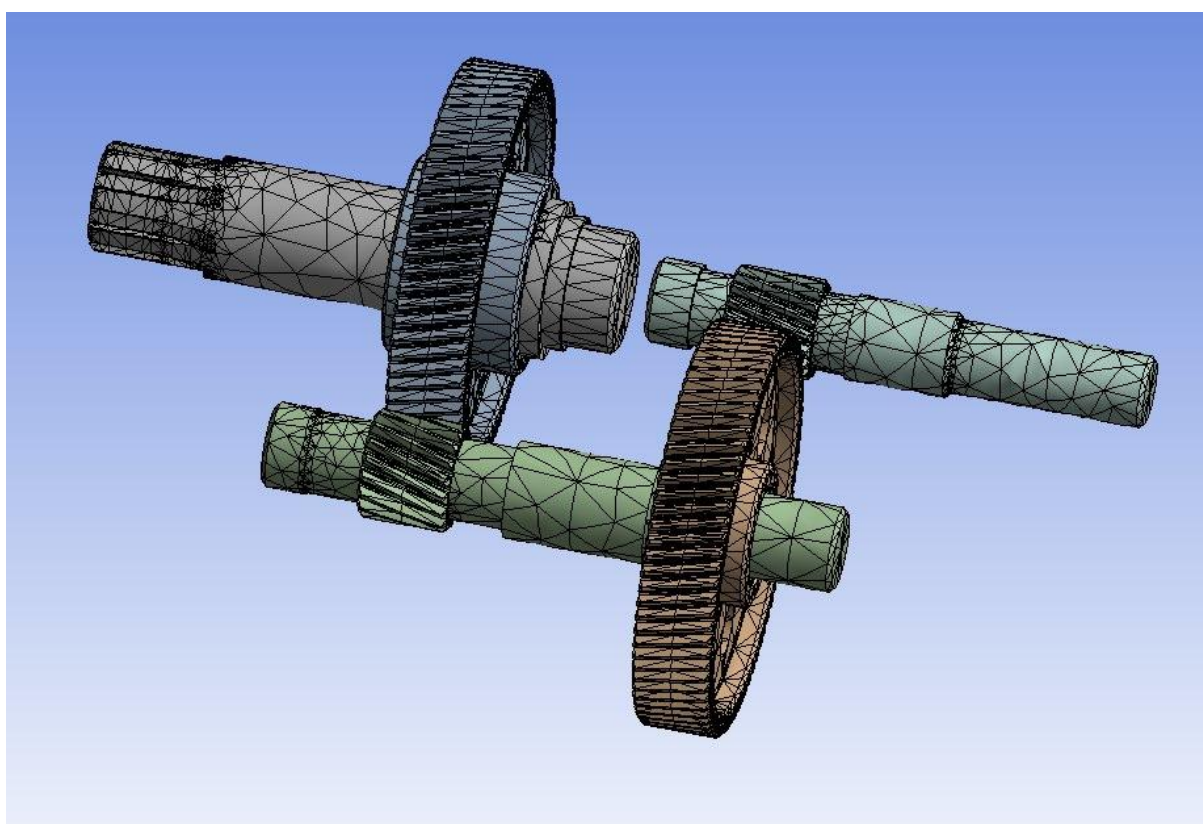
Сетка конечных элементов на 3D-модели цилиндрической зубчатой двухступенчатой передачи.
